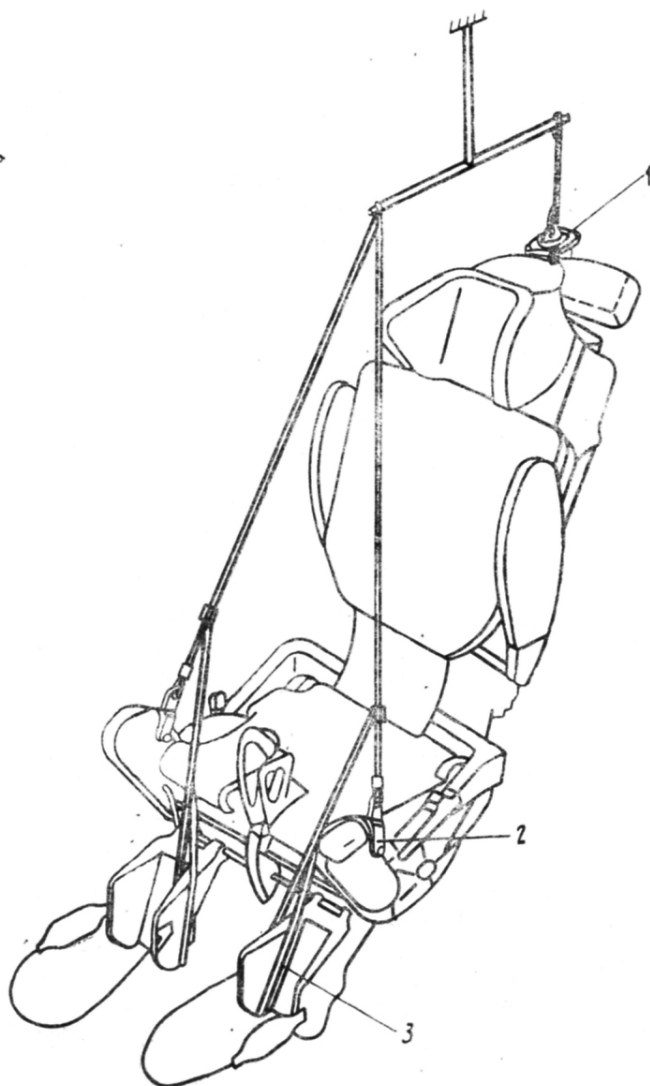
Подвеска кресла на стропях подъемного крана: 1—замок; 2—крепление за втулки на щитках чашки кресла; 3—фиксация опор ног
